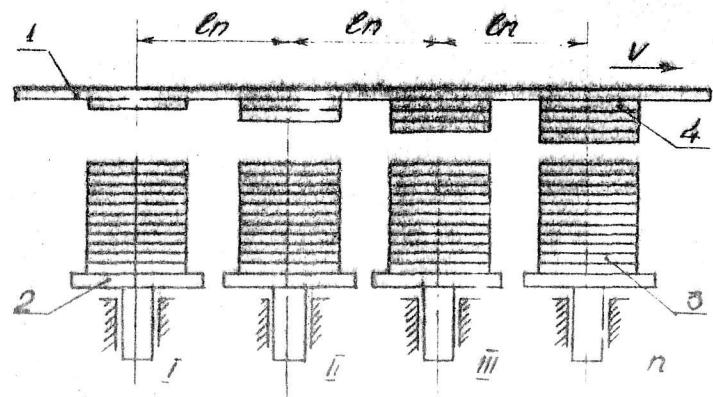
Принципиальная схема автоматической сборки деталей верха обуви
